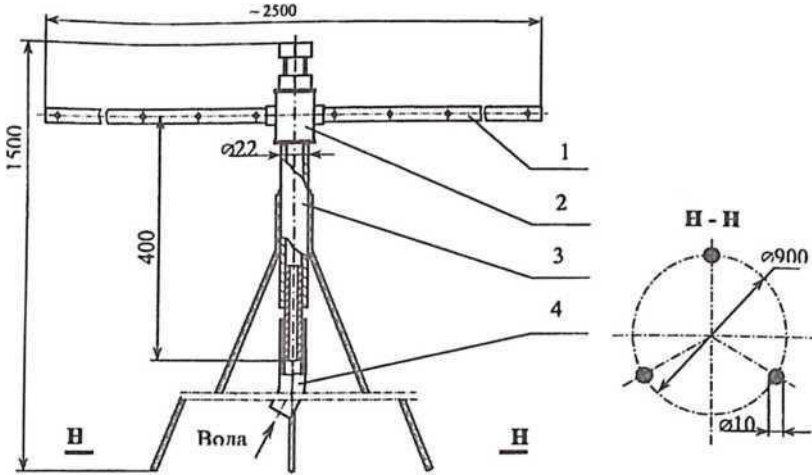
Розбризувач пропелерного типу: 1 - змінні штанги; 2 - обертова опора (маточний); 3 - опорна зварна стойка штативного типу; 4 - гумовий шланг.
